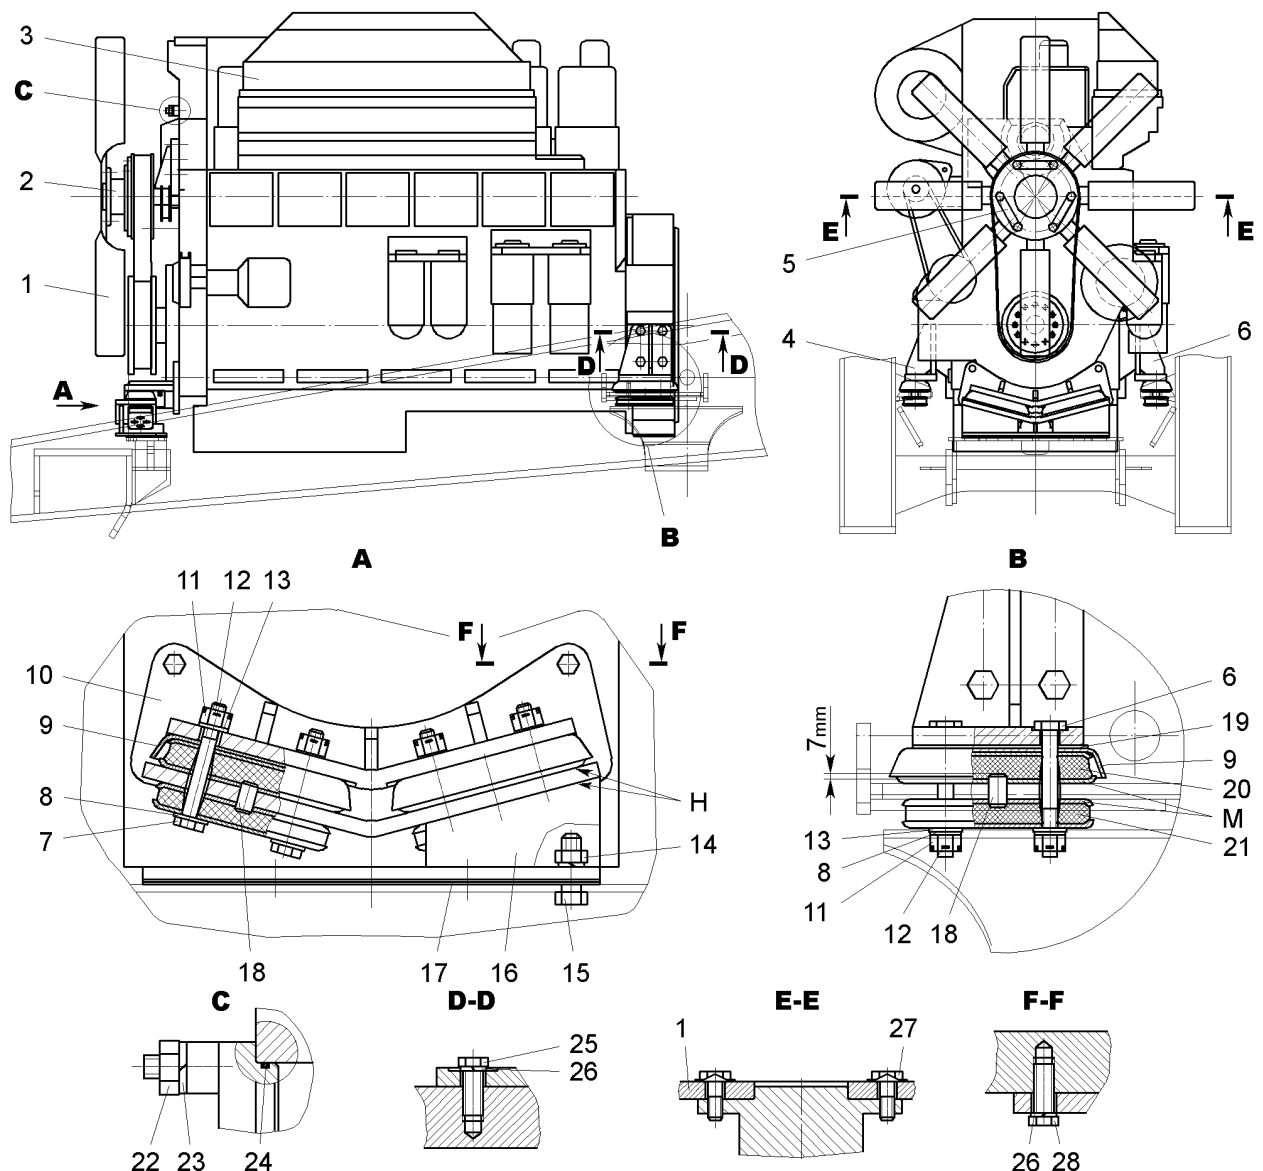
Установка двигателя самосвала БелАЗ-75453:
